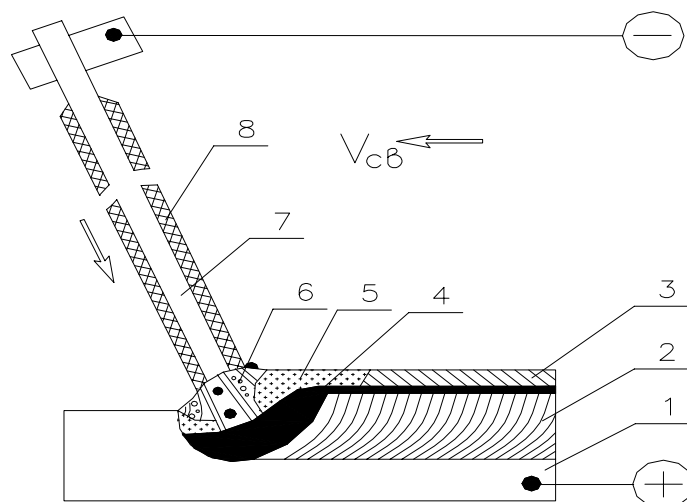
Схема сварки металлическим электродом открытой дугой:
